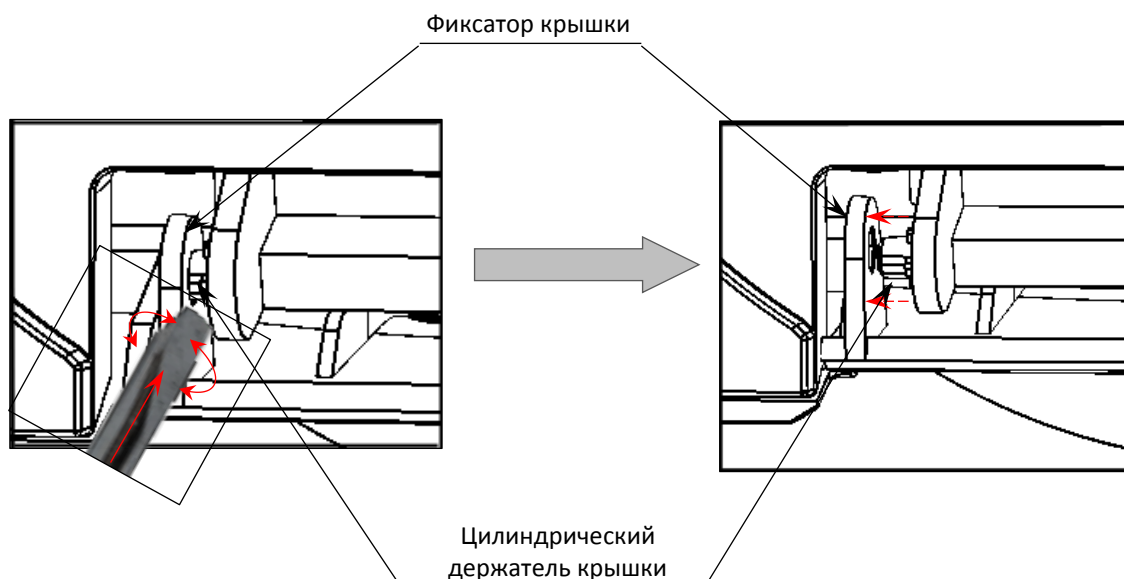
Снятие фиксатора крышки лотка с цилиндрического держателя
